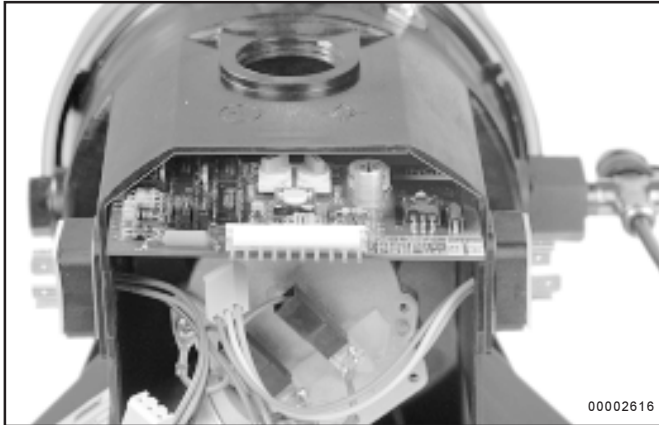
Steuerplatine im Gehäuse eingebaut
